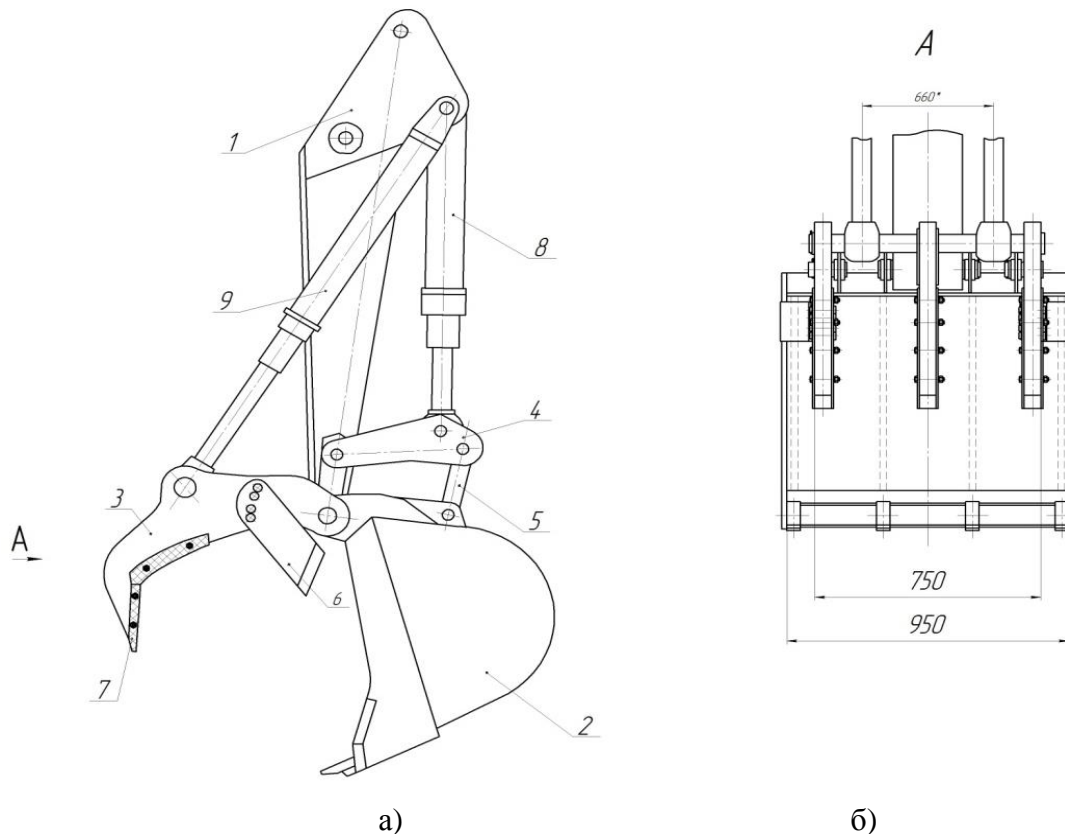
Общий вид рабочего оборудования: а – главный вид; б – вид слева
